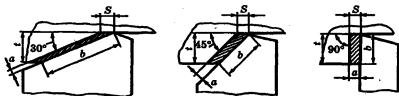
Формы поперечного сечения срезаемого слоя при обработке резцами с различными углами ϕ
